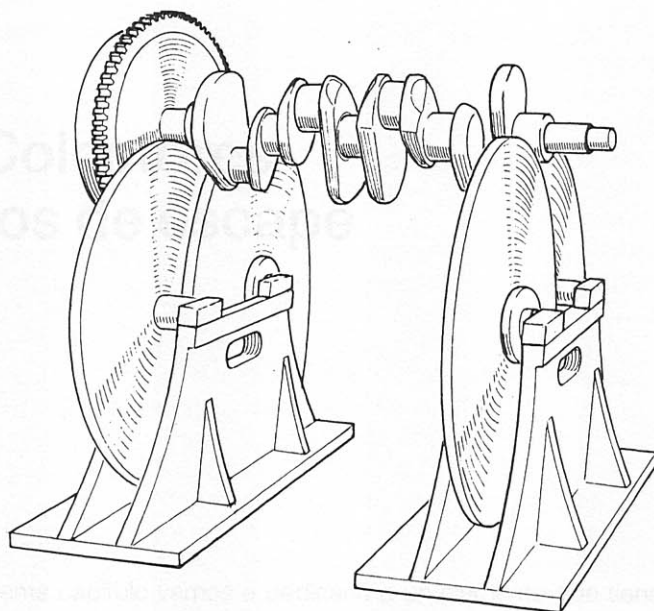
Equilibrado estático de un conjunto de cigüeñal con su volante de inercia montado y la parte de arrastre del embrague, montado sobre discos de soporte.
